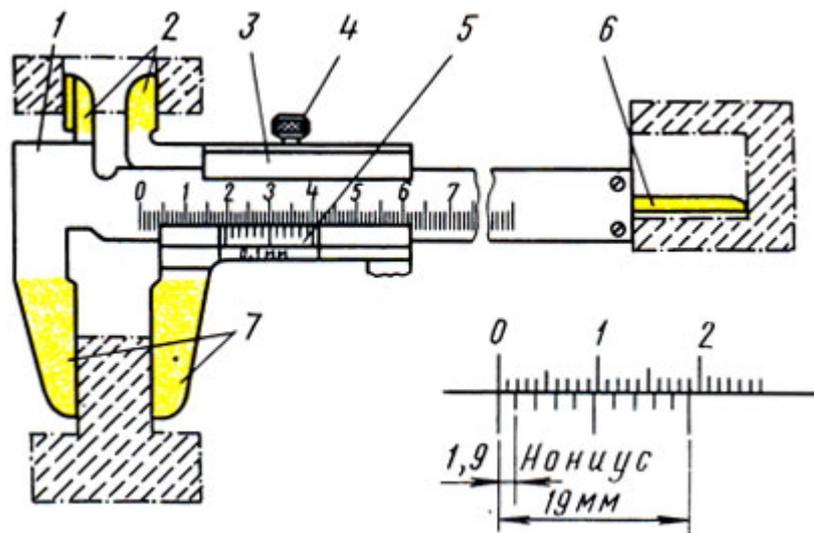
Штангенциркуль ШЦ-I: 1 - штанга, 2,7 - губки, 3 - подвижная рамка, 4 - зажим, 5 - шкала нониуса, 6 - линейка глубиномера
